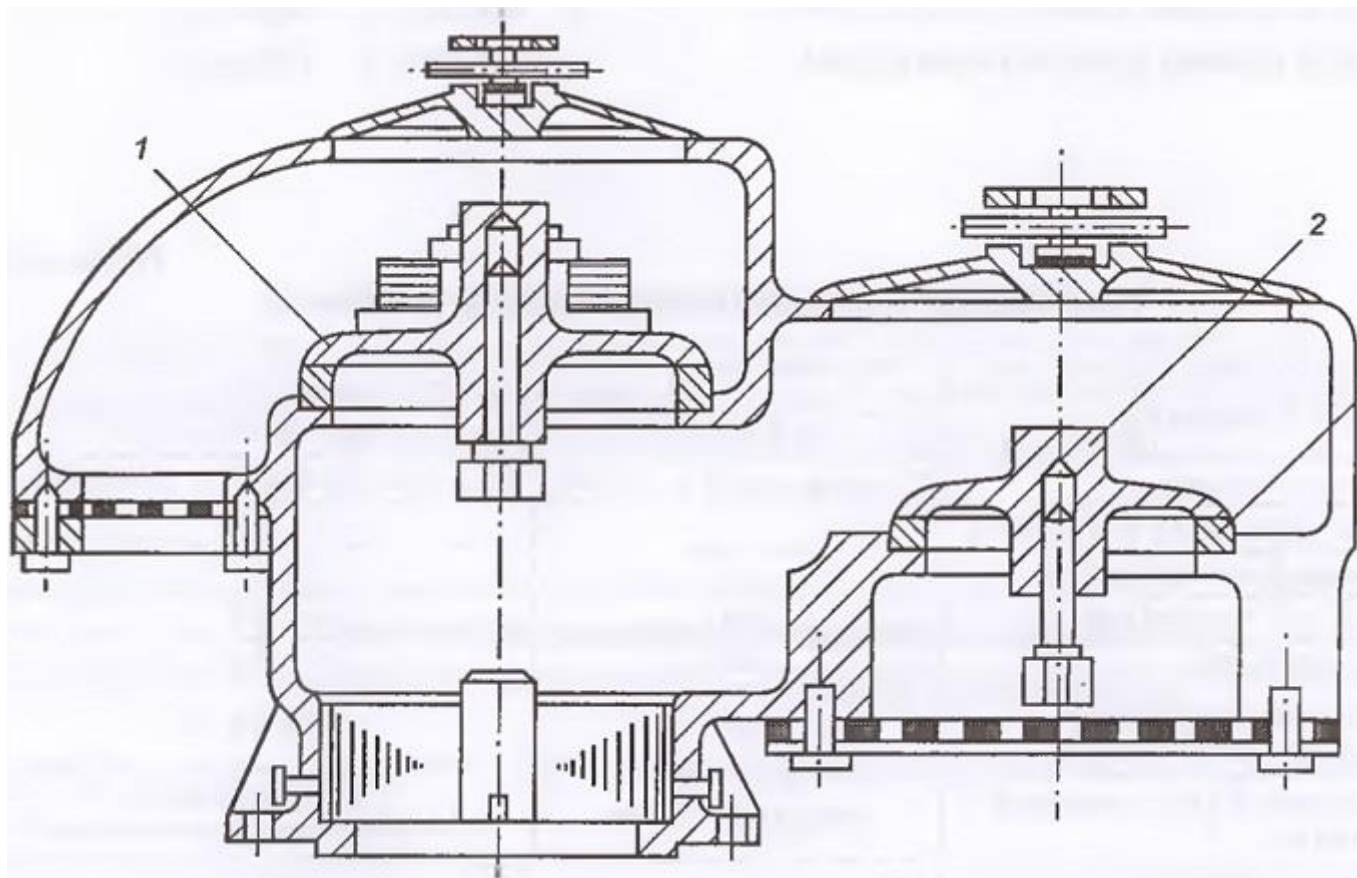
Обратный клапан: 1 - корпус; 2 - тарелки;
